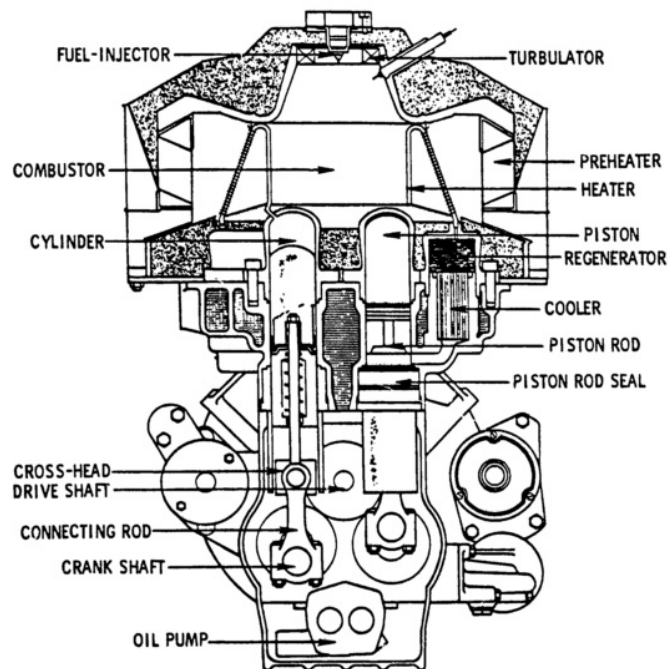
Ejemplo de un motor Stirling cinemático [52].
